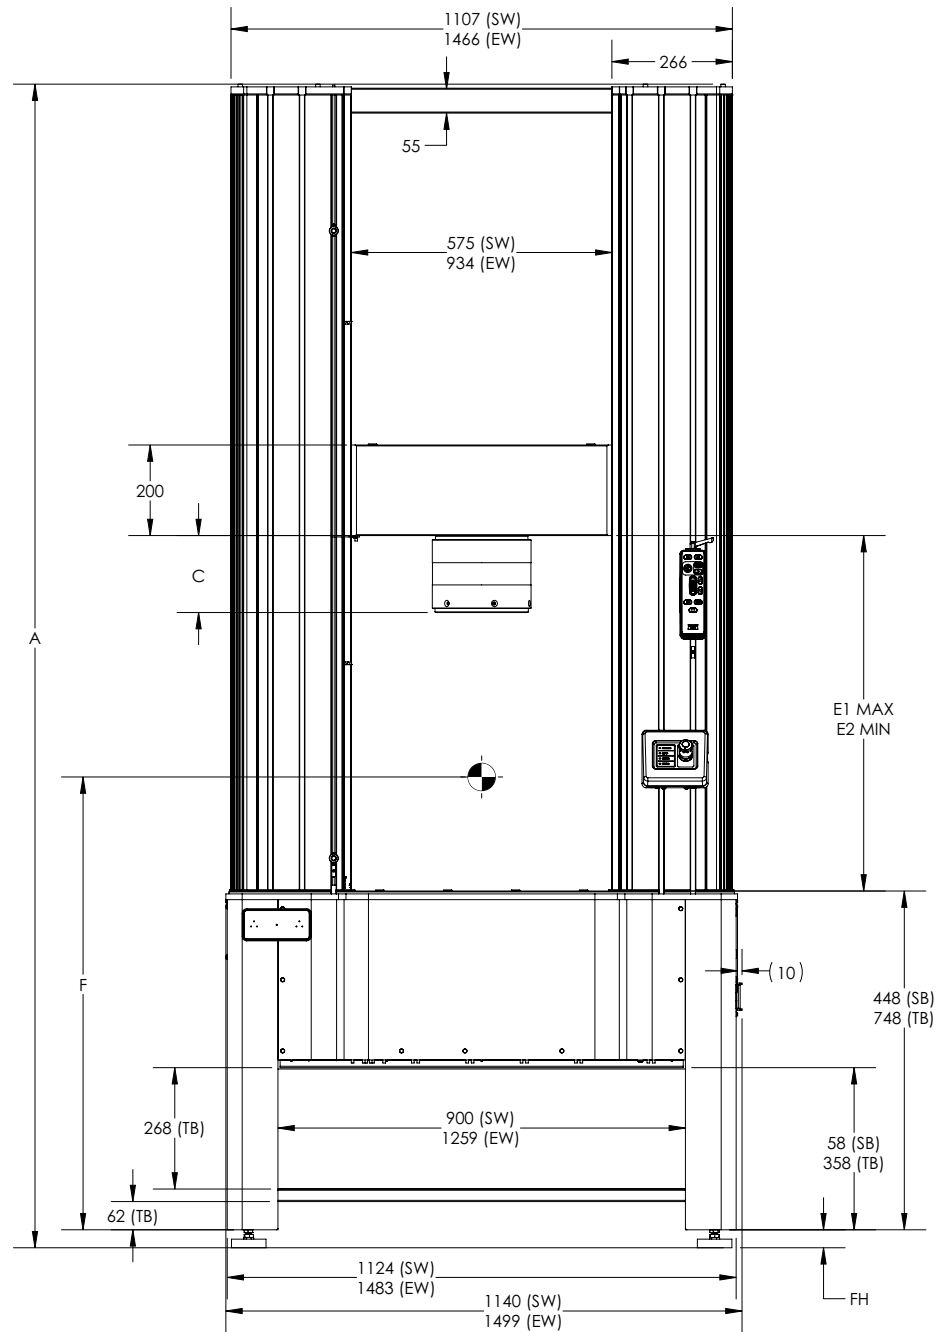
68FM-300 Dimensions du bâti – vue de face
